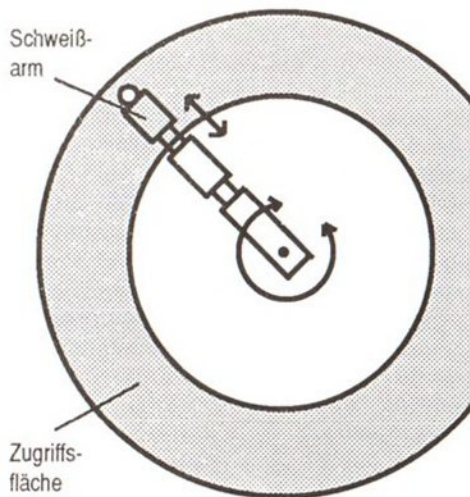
Zugriffsfläche des Schweißroboters.
